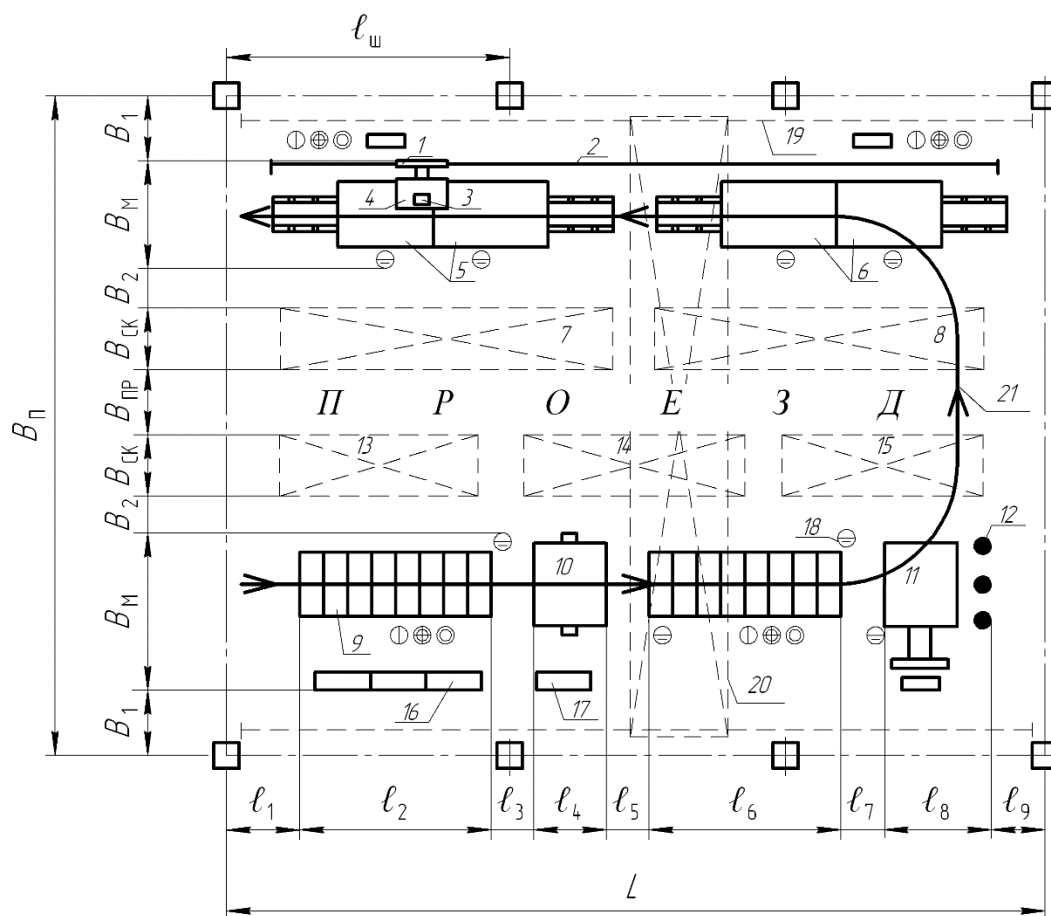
Планировка участка заготовки, сборки и сварки обечаек:
